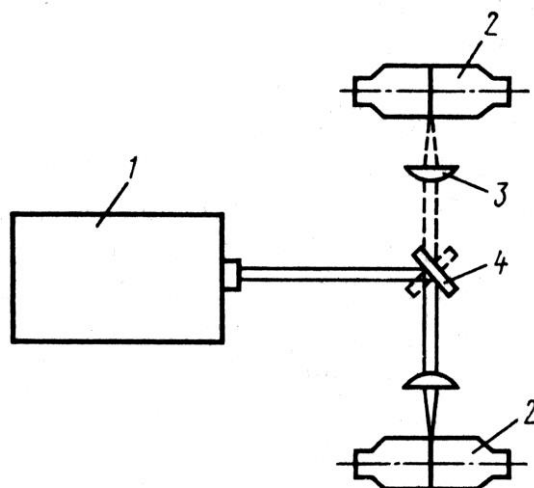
Схема сварки одним лазерным источником на нескольких рабочих местах: 1 – лазер; 2 – рабочие места; 3 – фокусирующая оптика; 4 – поворотное отклоняющее зеркало
